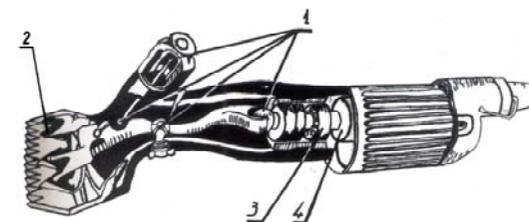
Точки смазки стригальной машинки МСУ-200: 1 – сфера упорного стержня и центра вращения, ролик; 2 – режущая пара; 3 – полость подшипников; 4 – электродвигатель
